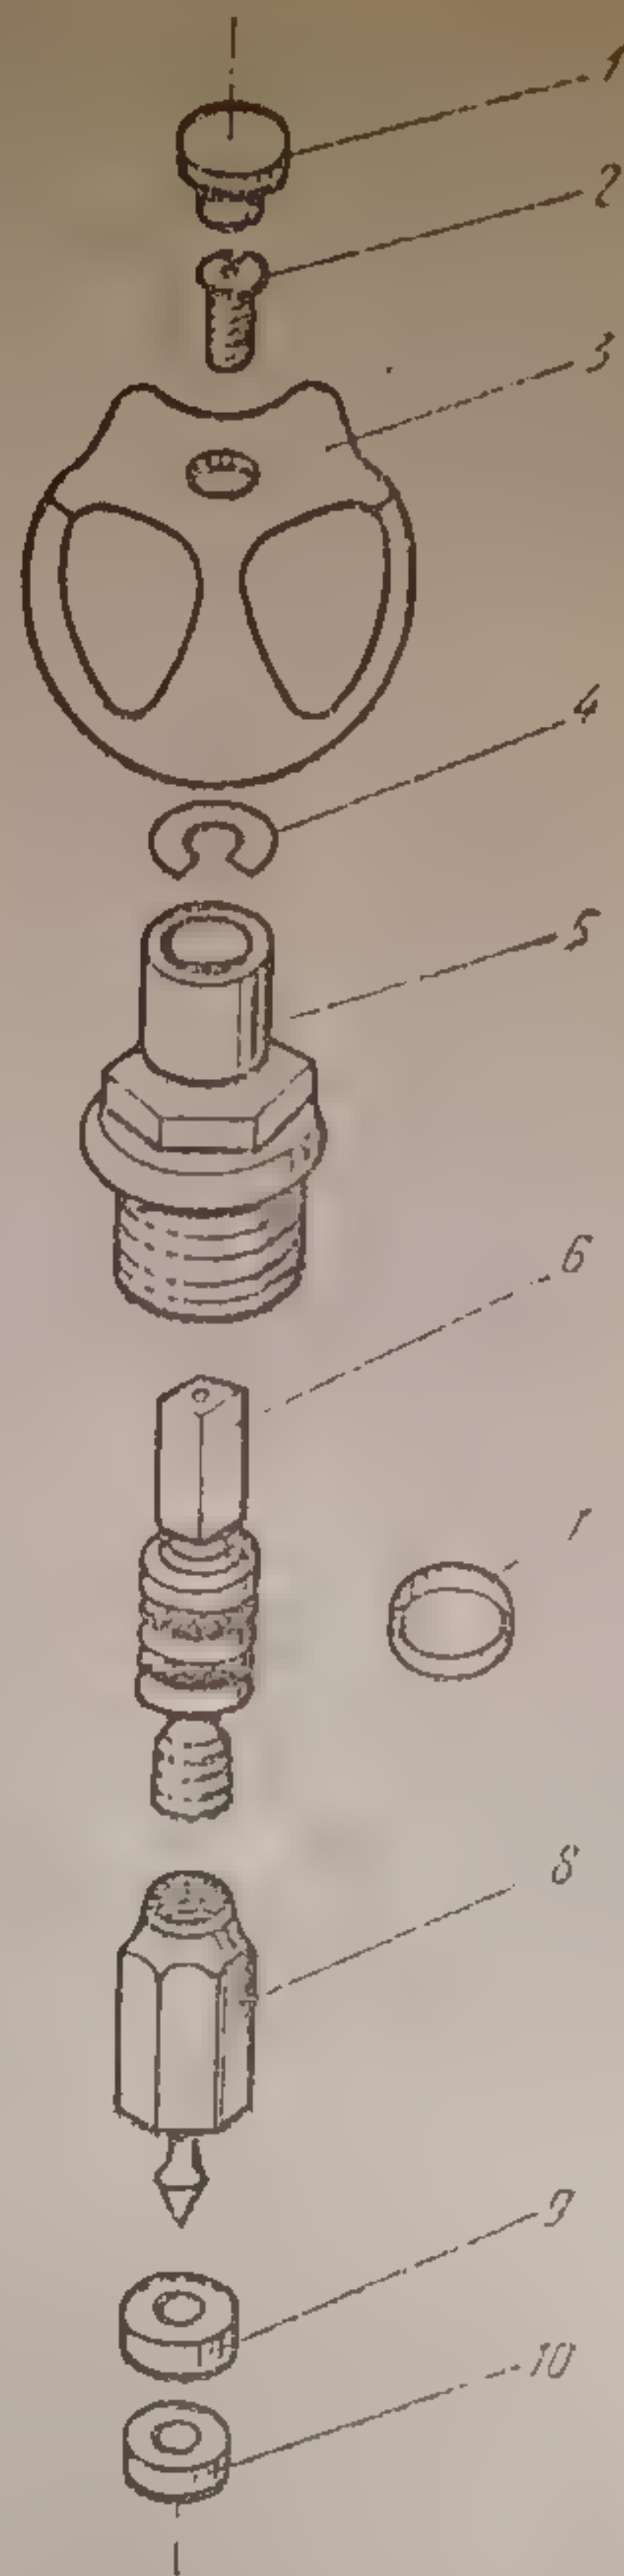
Головка крана с возвратно-поступательным движением: 1 — указатель; 2 — винт; 3 — маховик; 4 — стопорная шайба; 5 — корпус; 6 — шток; 7 — сальник; 8 — шпindel; 9 — клапан; 10 — прокладка
